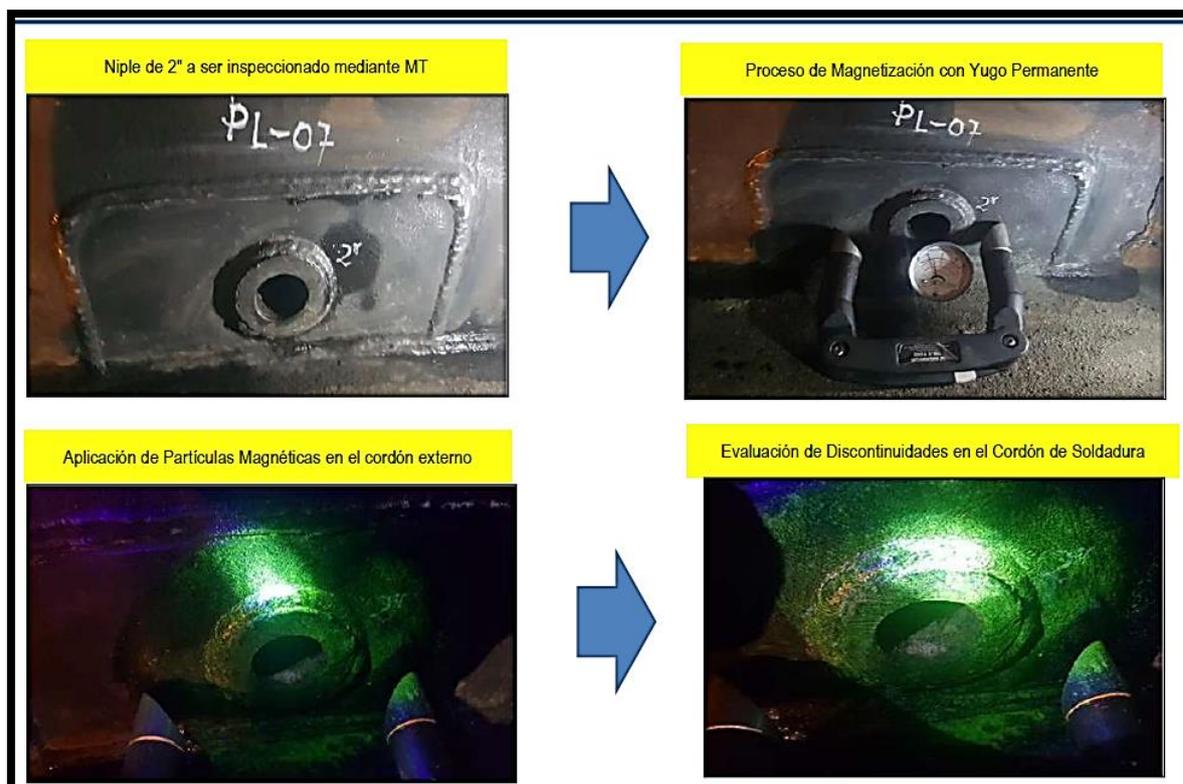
Uniones soldadas cordón externo-Partículas magnéticas
